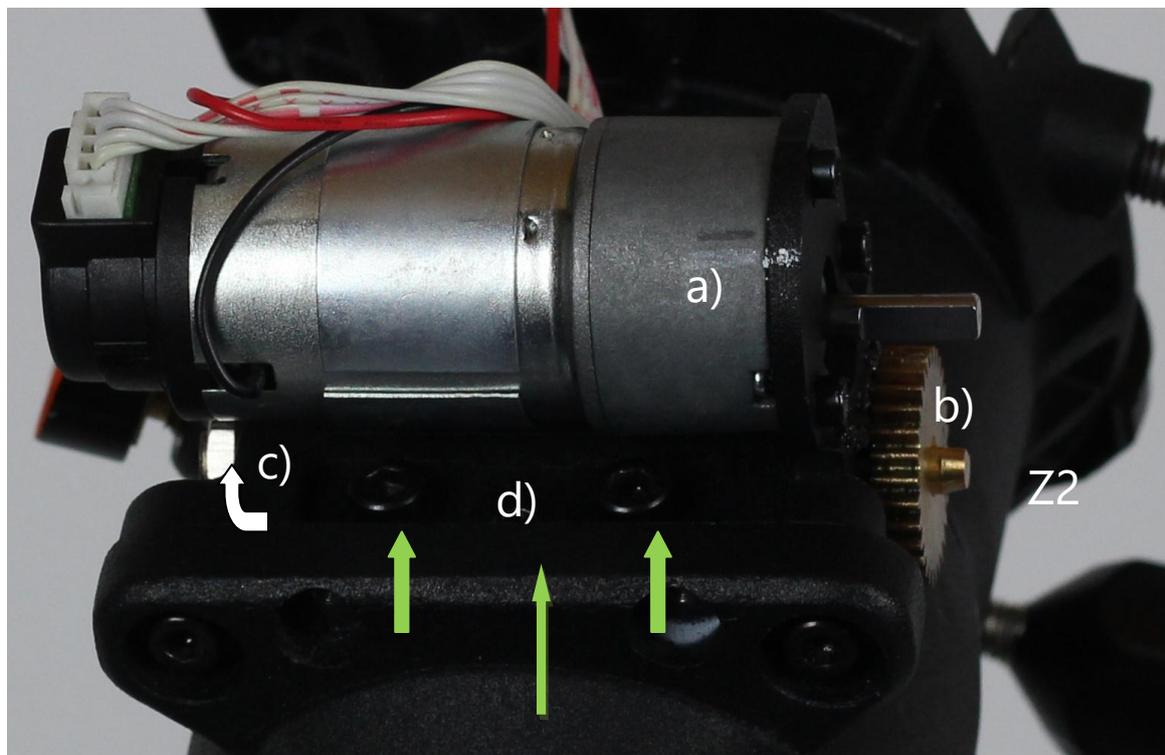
Beispiel AVX, in Grün markierte Justierschrauben für die Schnecke und Konterung
